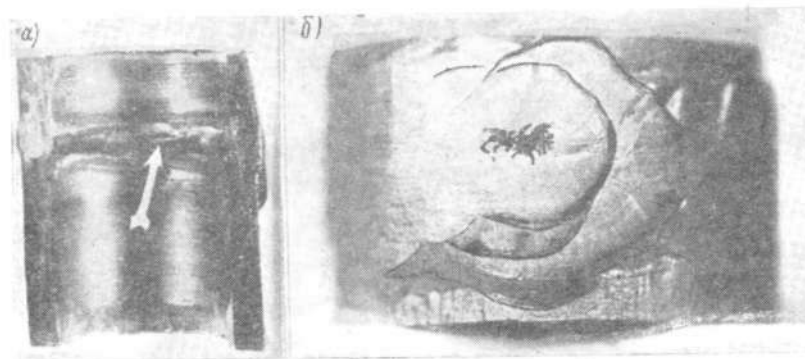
Кратеры в сварных швах: а — при автоматической сварке вольфрамовым электродом; б — при ручной дуговой сварке.
